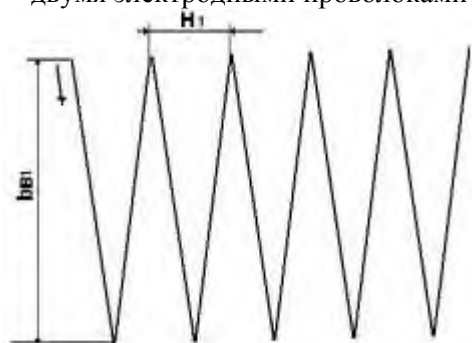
Способ ширококослойной наплавки порошковой лентой
